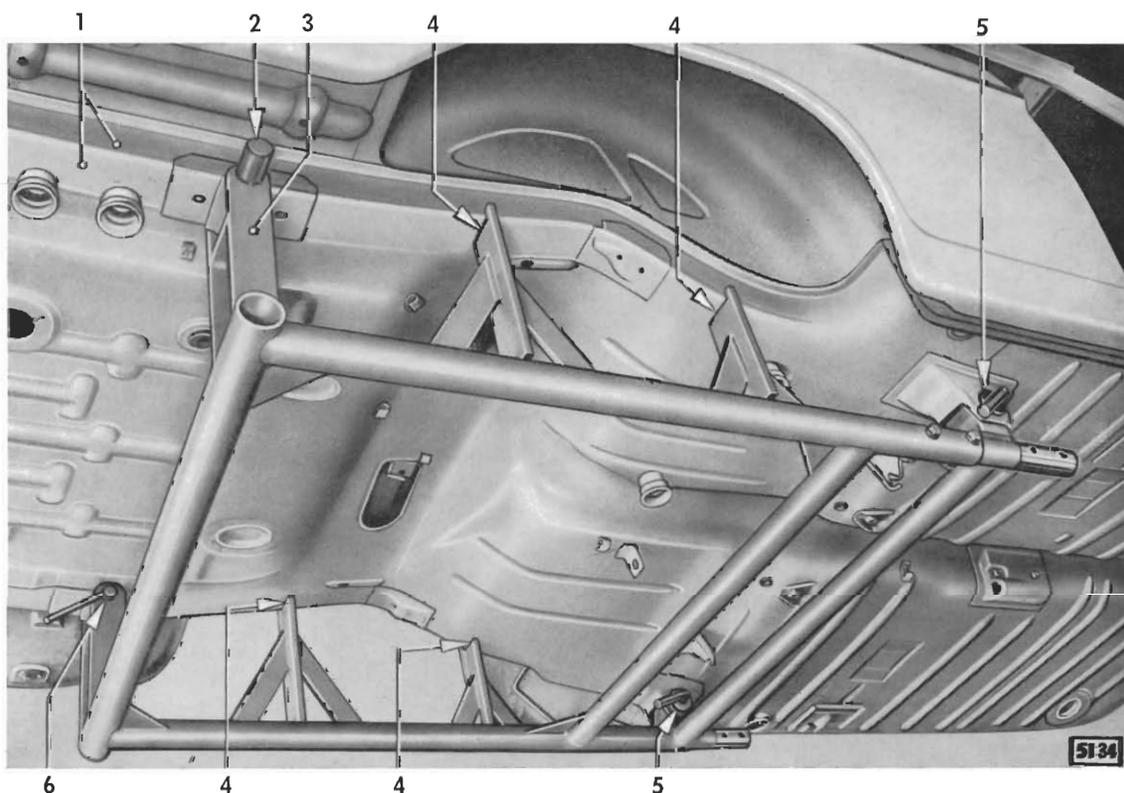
Kofferraumbodenprofil an Hinterlängsträger-Schweißlehre angepaßt
